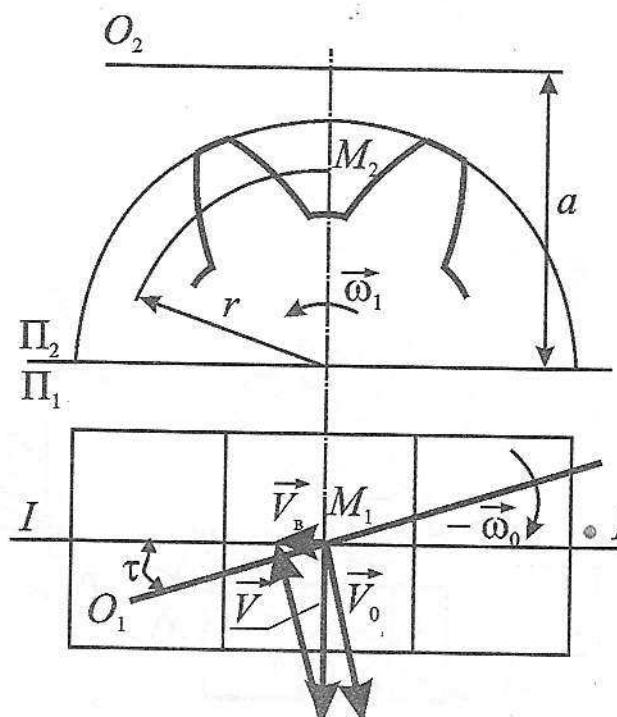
Схема формообразования обкаточными дисковыми фрезами много зубьевых деталей
